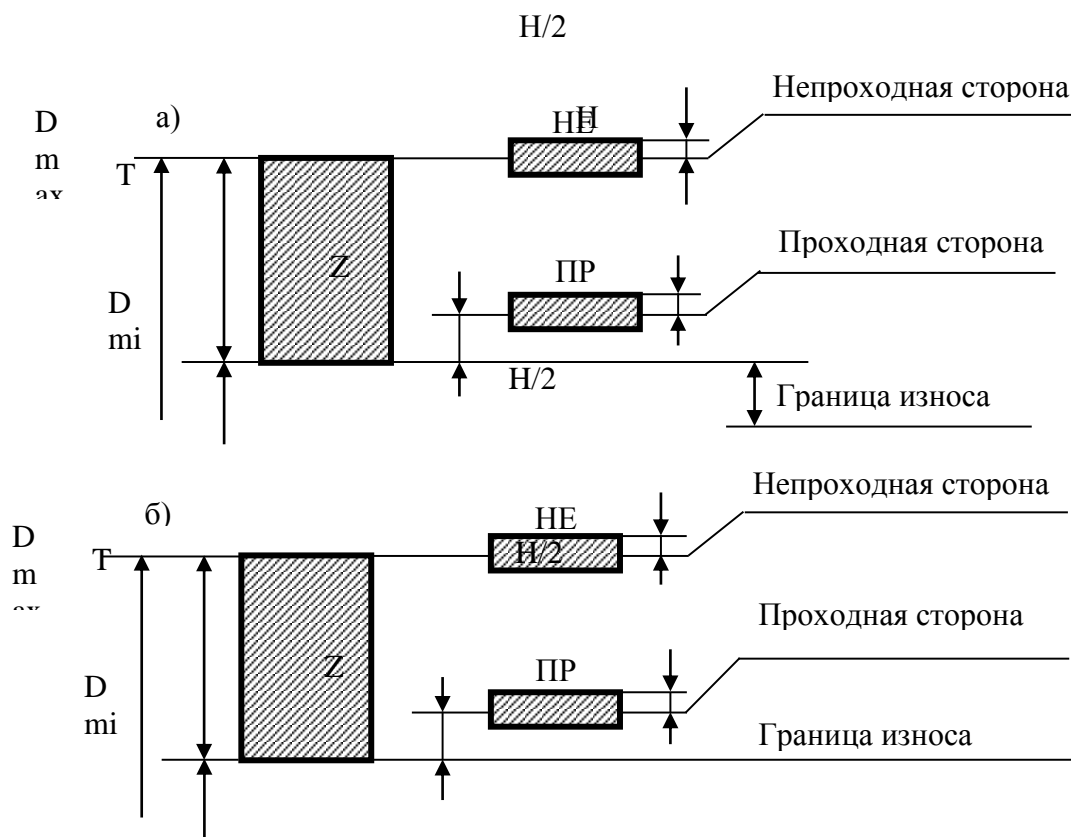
Расположение полей допусков рабочих (ПР и НЕ) калибров-пробок для контроля отверстий размерами до 180 мм
